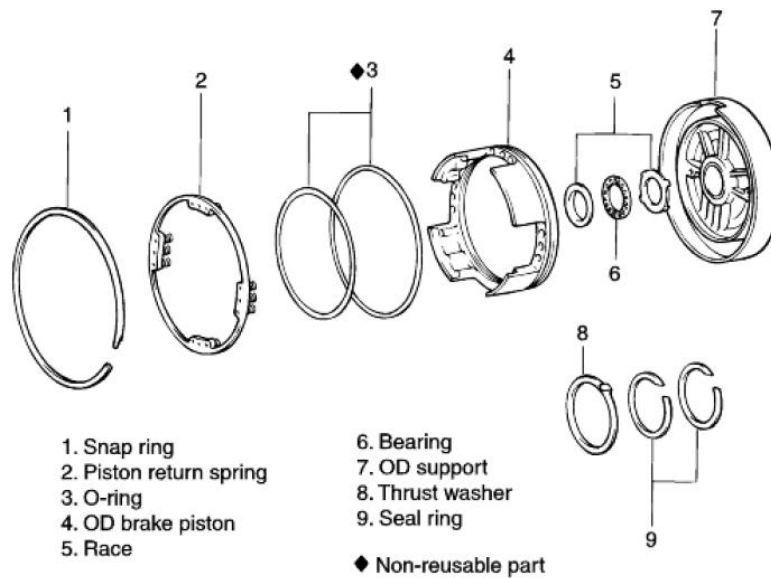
B0: B0: O/D brake - Hold O/D sun gear.¹⁹
